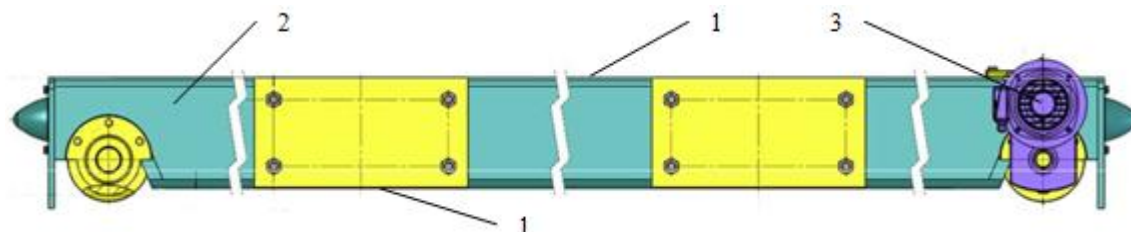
Общий вид типовой металлоконструкции концевой балки двухбалочного мостового крана: 1 — верхний и нижний пояс; 2 — вертикальные стенки; 3 — ходовая часть крана
